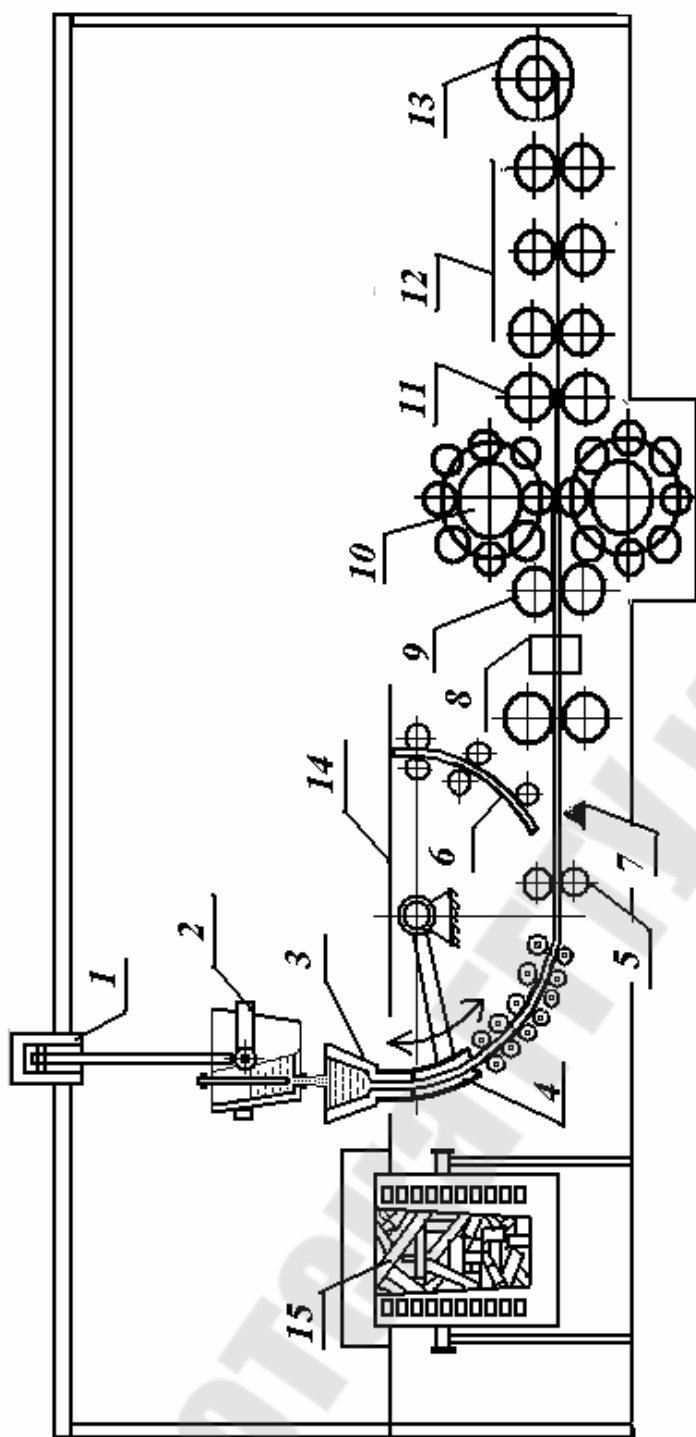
Схема разреза участка литейно-прокатного агрегата с планетарным станом. 1-мостовой кран; 2-ковш; 3-промехуточная емкость (воронка); 4-кристаллизатор; 5-тянущее устройство; 6-затравка; 7-летущие ножницы; 8-индуктор; 9-задающая клеть; 10-планетарная клеть; 11-тянущие ролики; 12-клеть продольной прокатки; 13-моталка; 14-рабочая площадка; 15-индукционная печь.
